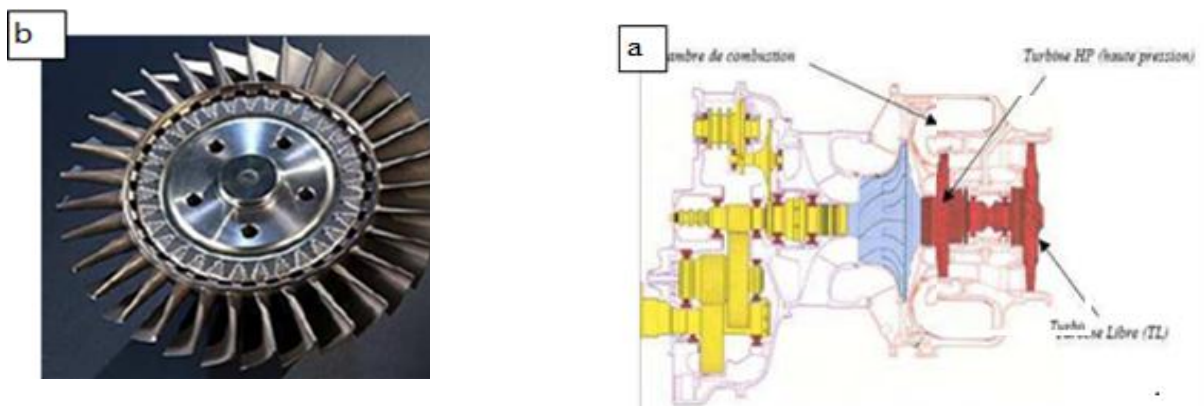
Coupe de turbomachine de type Arrius (a), disque de turbine HP avec ses aubes(b) [réf. Turboméca].
